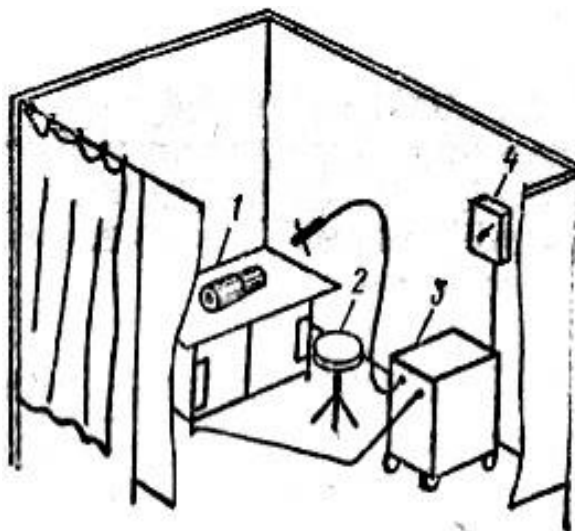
Кабіна для стаціонарного зварювального поста: 1 – стіл; 2 – стілець; 3 – зварювальний апарат; 4 – пусковий апарат
